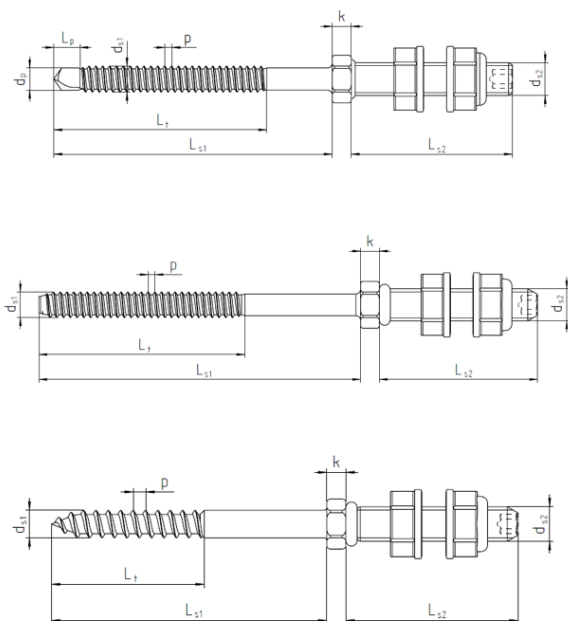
Befestigungsschrauben mit angeschweißtem Gewindestift
